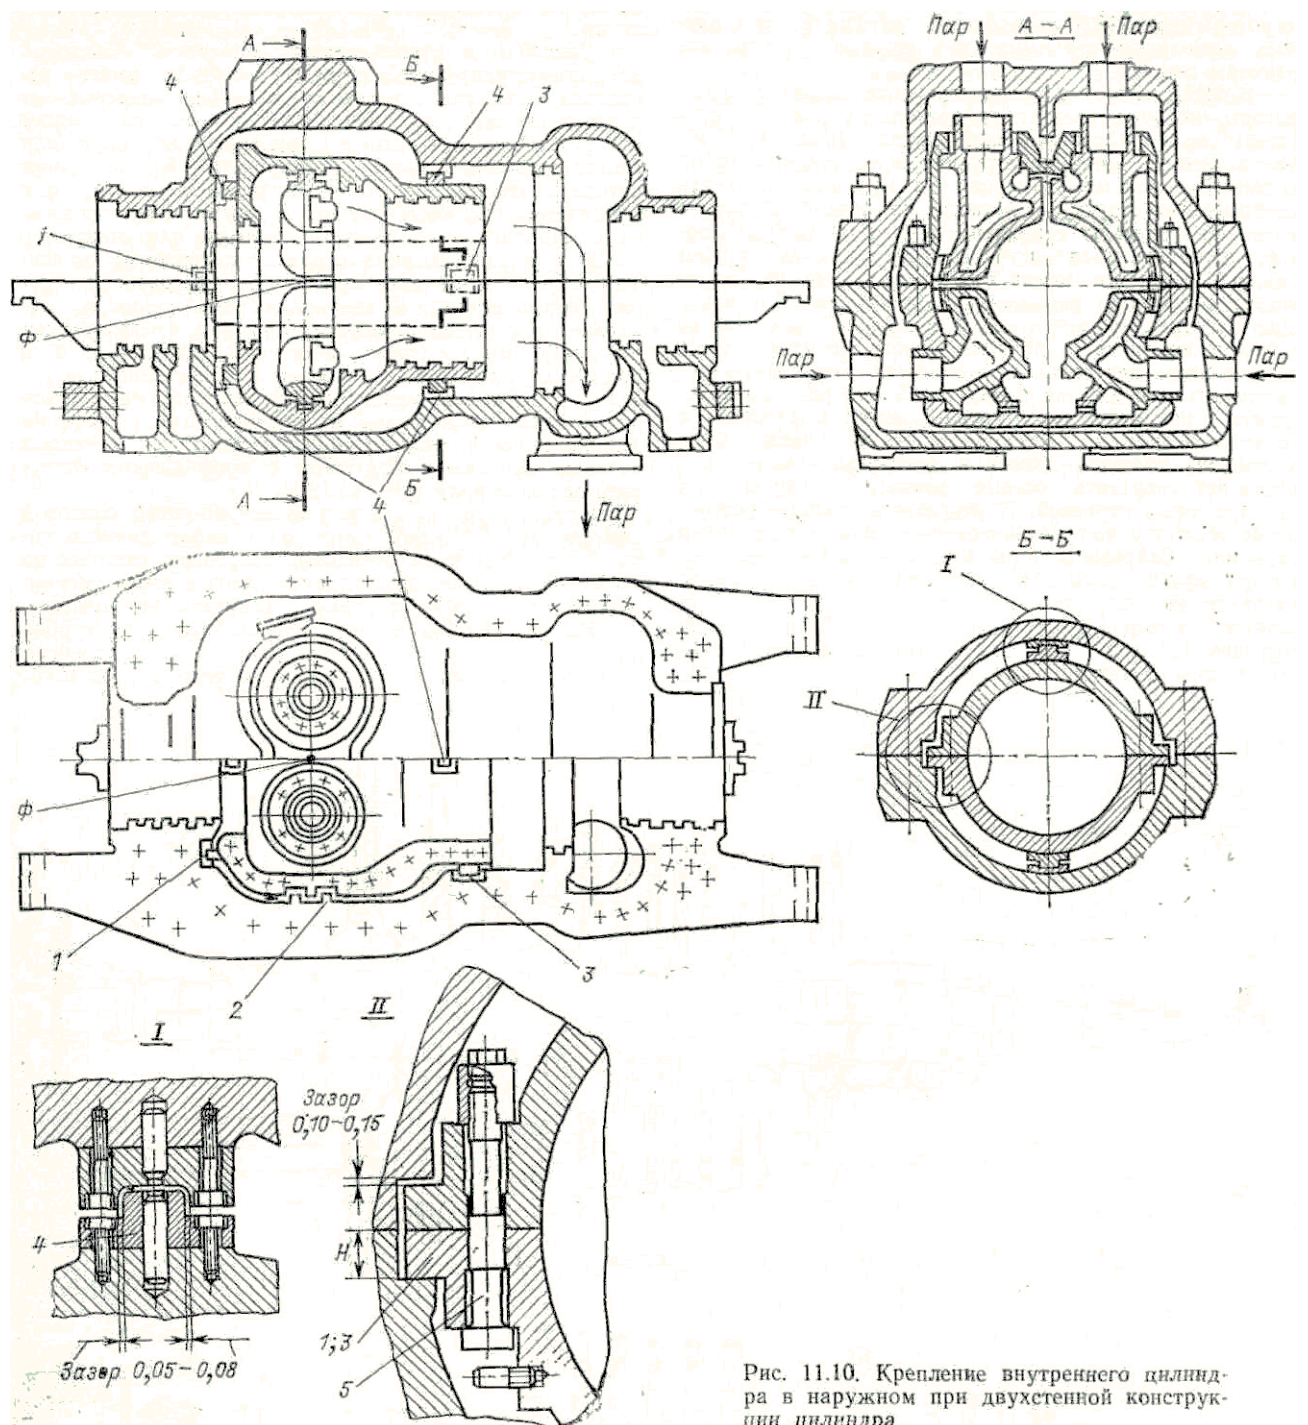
Крепление внутреннего цилиндра в наружном при двухстенной конструкции цилиндра
